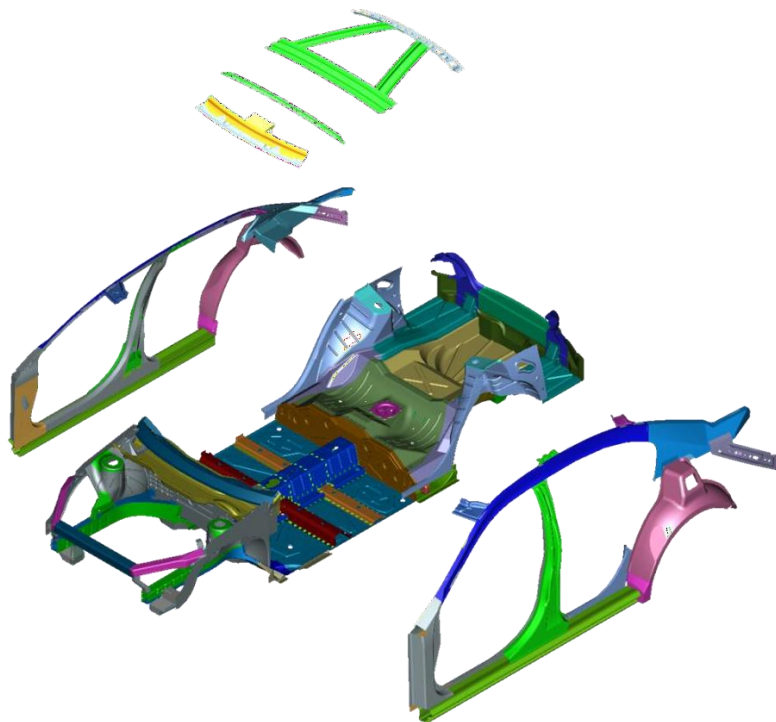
Монтажна ділянка два для звареної точковою зваркою конструкції.
